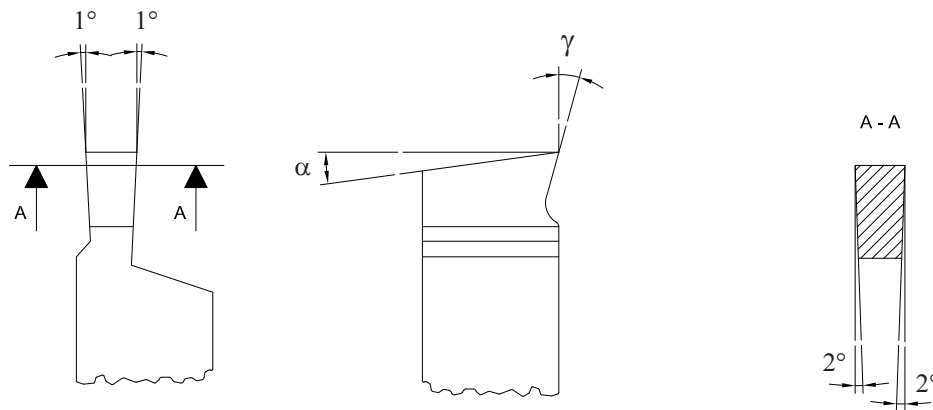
Negatieve openingshoek voor voorbereiding
